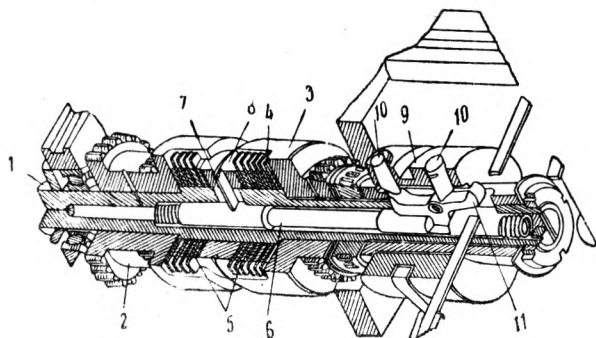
Фрикционная муфта токарного станка ДИП-200
